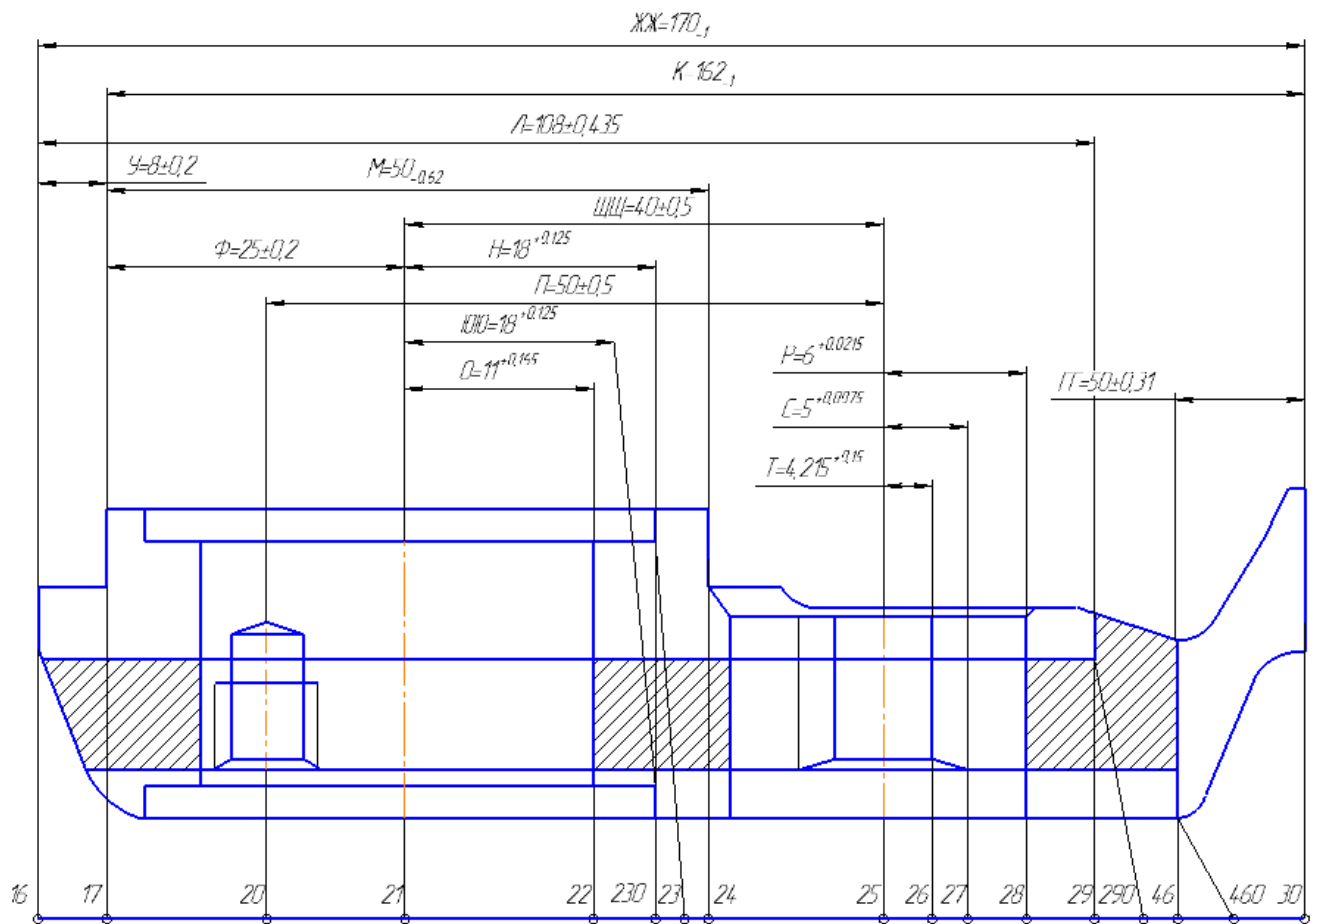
Преобразованный чертеж детали в третьей проекции
